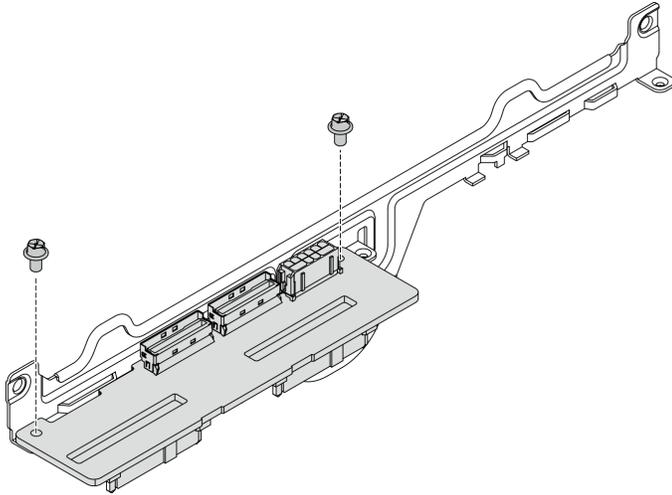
Installation du fond de panier d'unité 2,5 pouces au module
